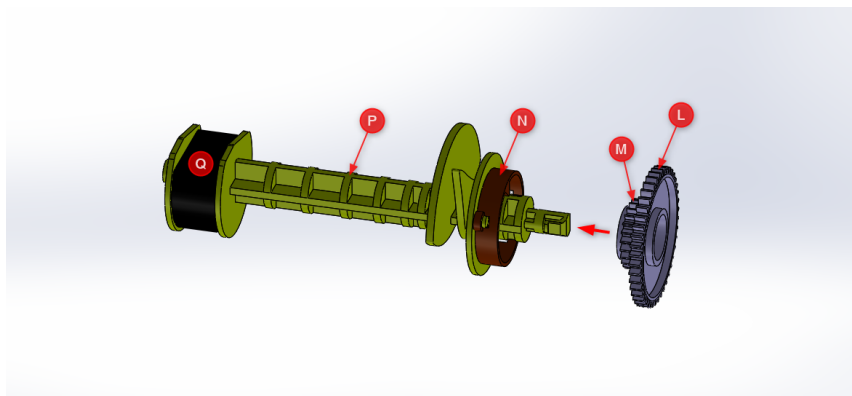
Montaje del conjunto rueda dentada (L) y rueda de trinquete (M) sobre rodillo alimentador de hoja (P)
